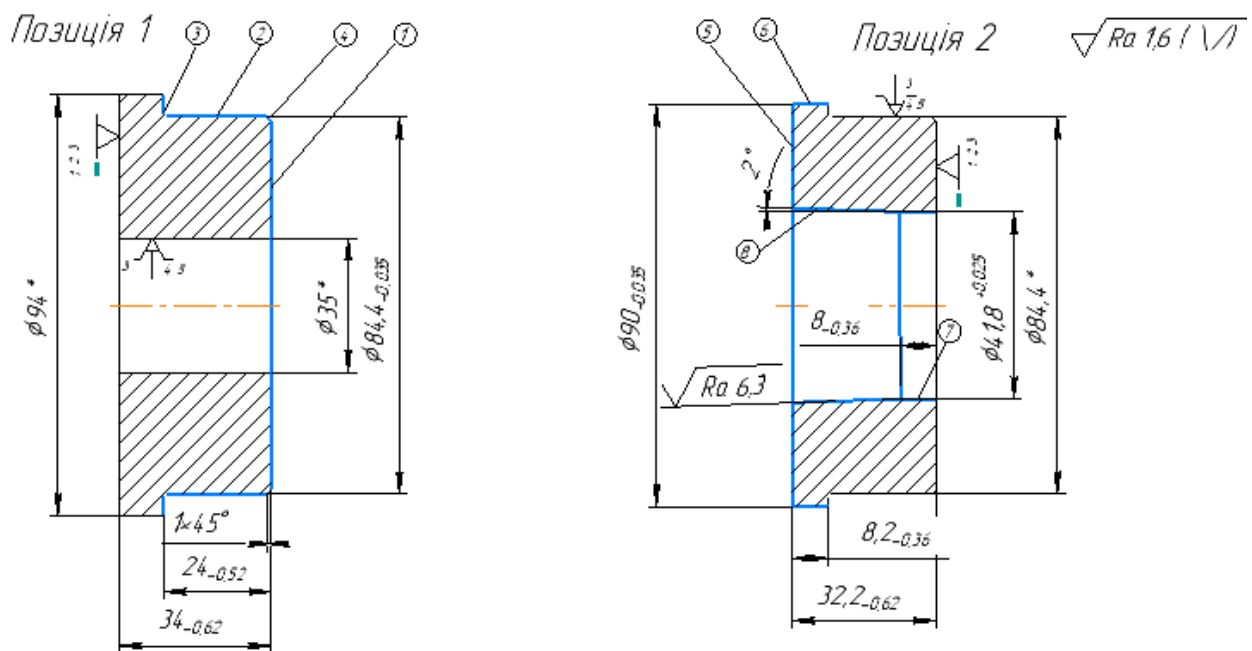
Альтернативна схема базування заготовки для операції 025
